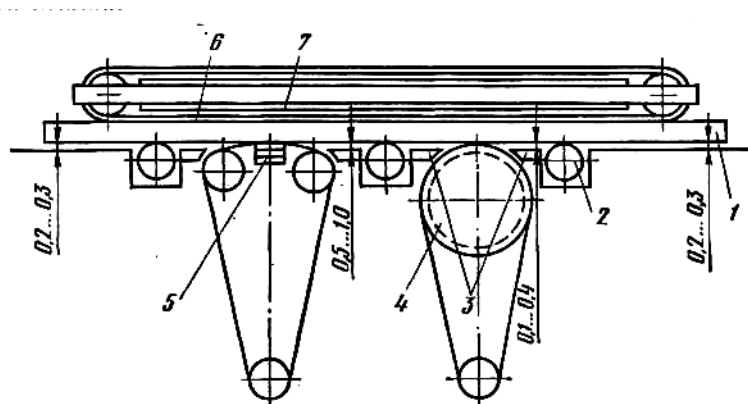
Схема настройки широколенточного шлифовального станка: 1 — шаблон, 2 — опорный ролик, 3 — базирующие столики, 4 — контактный валец, 5 — контактная прижимная балка, 6 — конвейерная лента, 7 — опорный стол конвейера
